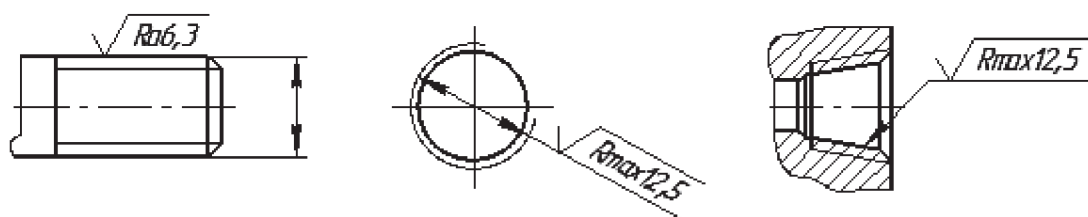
Обозначение шероховатости поверхностей профиля резьбы
